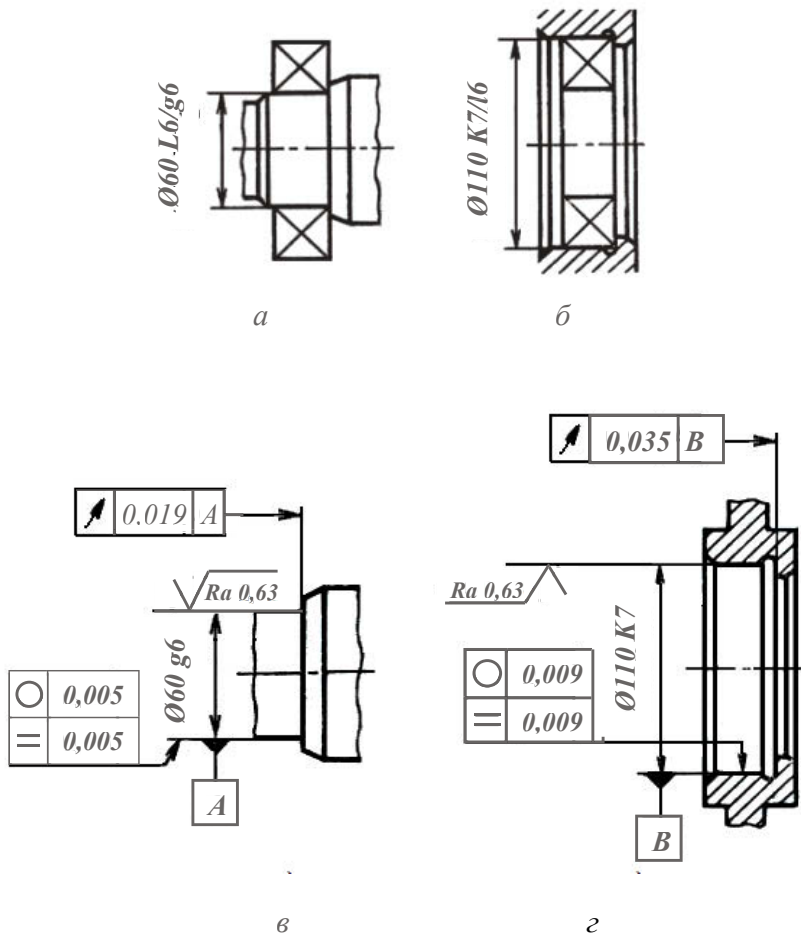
Эскиз сборочного узла с подшипниками качения и посадочных поверхностей вала и отверстия: а — посадка подшипника на вал; б — посадка подшипника в корпус; в — посадочная поверхность вала; г — посадочная поверхность корпуса
